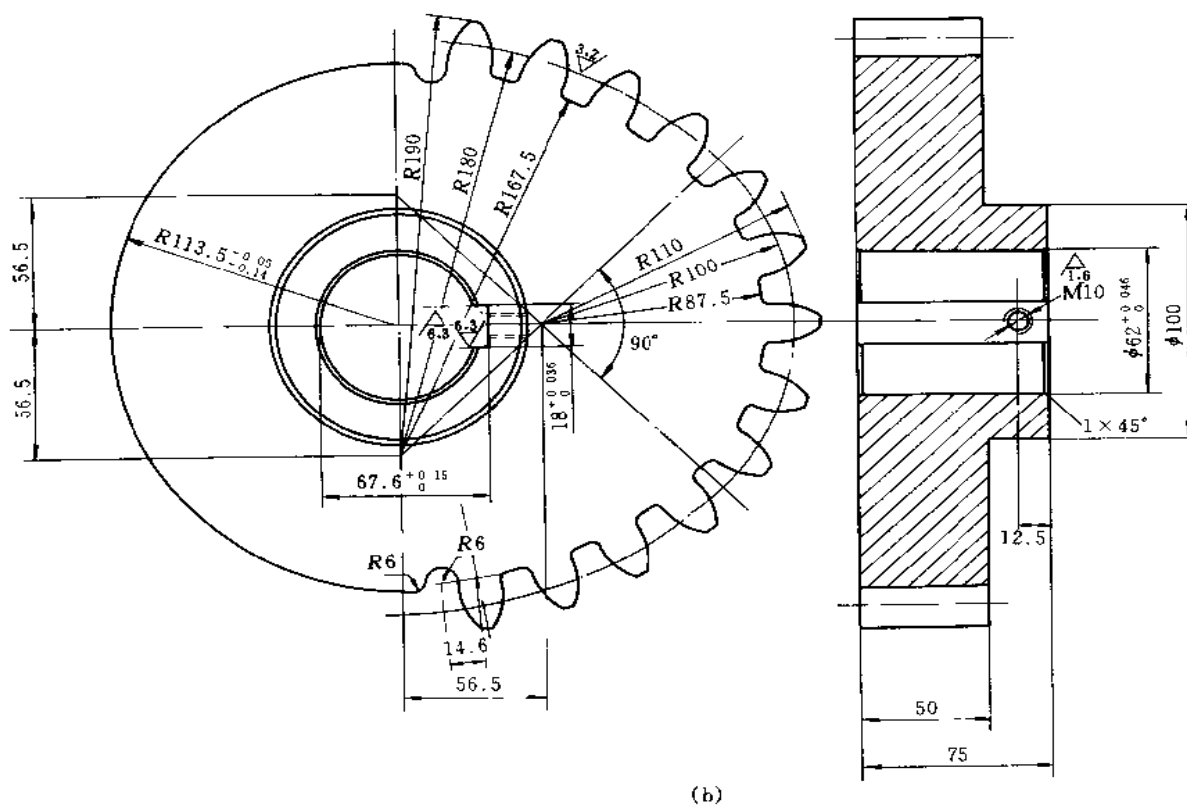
偏心圆齿轮-三叶卵圆齿轮机构
